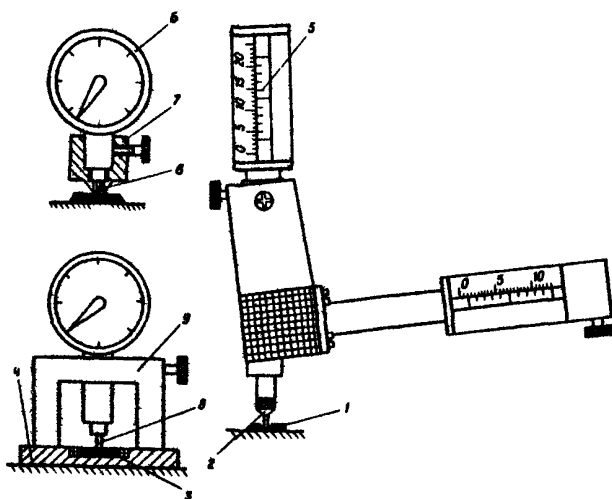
Сборка пробника Ш-2М для оценки твердости горных пород по шламу.
